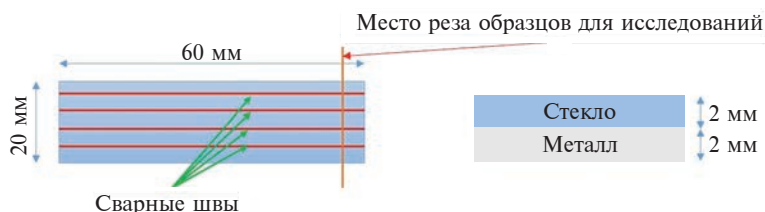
Эскизы образцов с указанием размеров и мест для исследований: а — вид сверху на образец, б — вид с торца.
